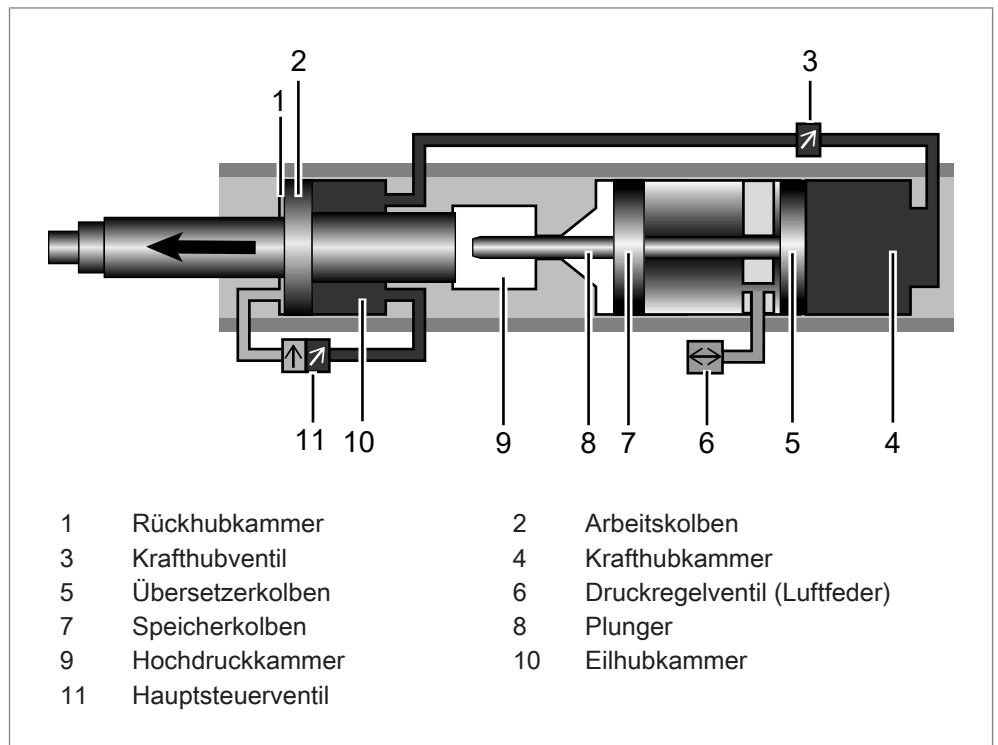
Krafthub Kraftpaket mit Druckregler-Luftfeder
